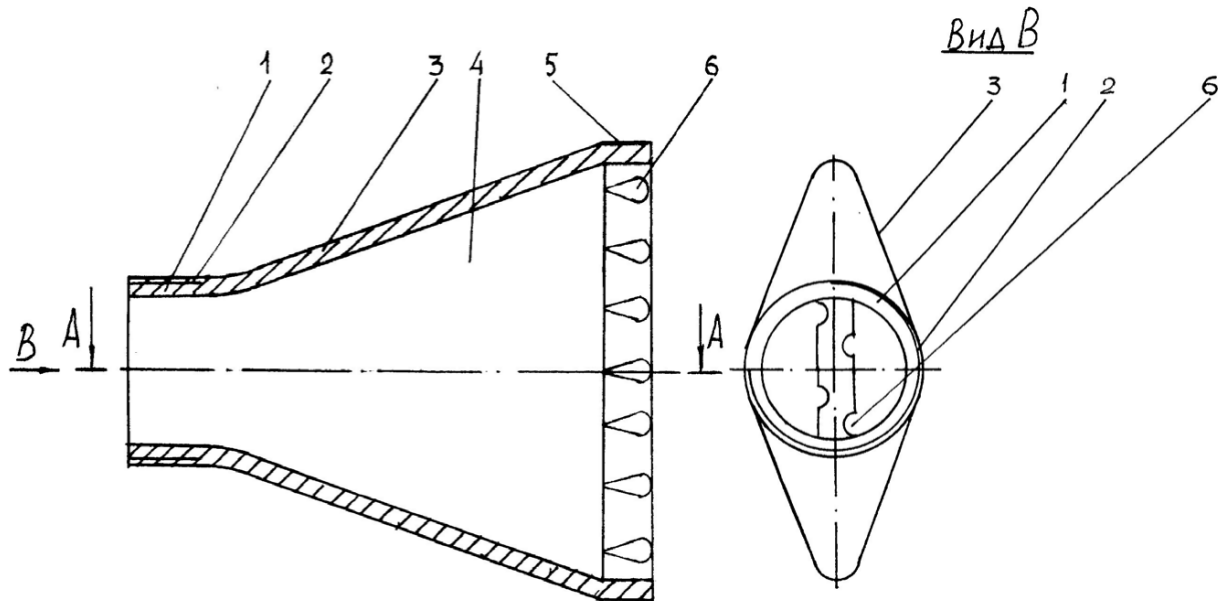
Схема щілинної дощувальної насадки: 1 – корпус; 2 – зовнішня різьба; 3 – трапецієподібний дифузор; 4 – розширювальна камера; 5 – горизонтальна обичайка; 6 – розсікачі потоку.
